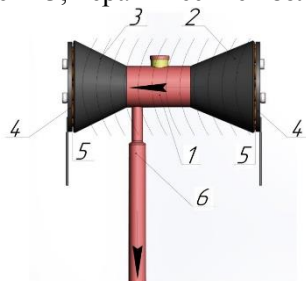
Схема крепления оснастки для УЗ обработки ЭВП: 1 – ЭВП; 2,3 – концентраторы УЗ излучателей; 4 – прижимные шайбы; 5 – пластины пьезокристалла; 6 – штенгельная трубка откачки
